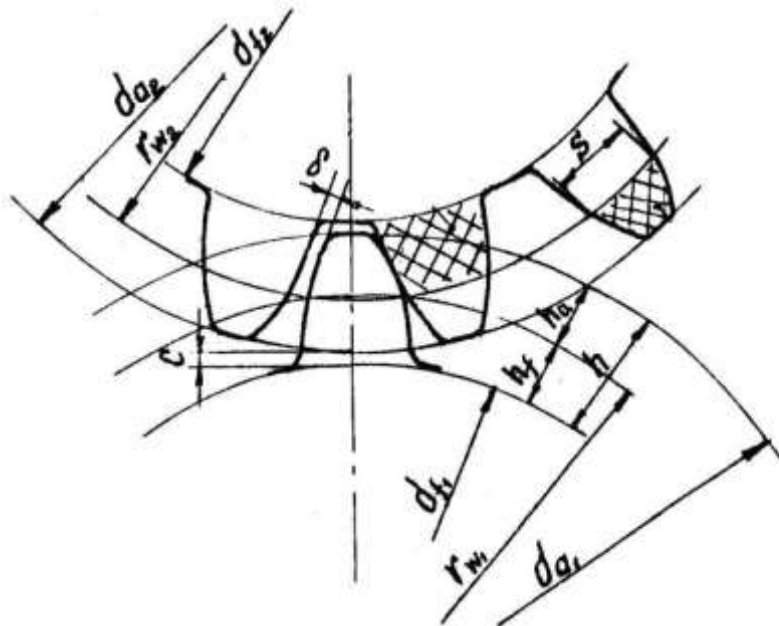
Схема зачеплень зубчастих коліс
